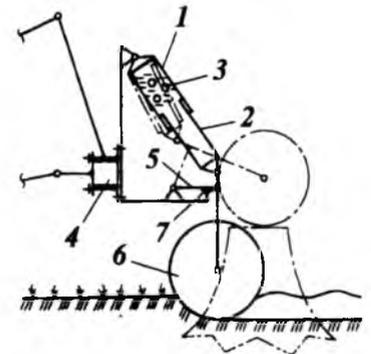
Кинематическая схема предохранителя дисковой бороны: 1 — цилиндр; 2 — пустотелый шток; 3 — герметичные упругие капсулы; 4 — рама; 5 — стойка дисковой батареи; 6 — дисковая батарея; 7 — ограничитель
